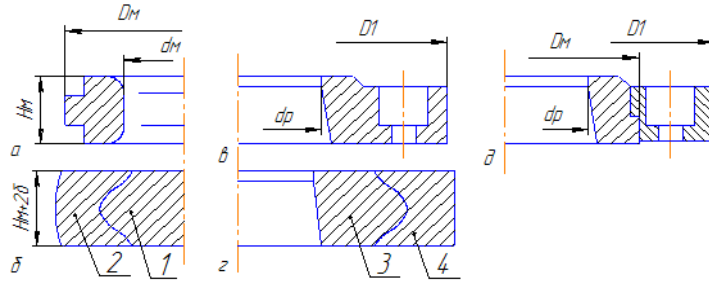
Вплив конструкції матриці на якість металу, з якого виготовляються її робочі елементи
